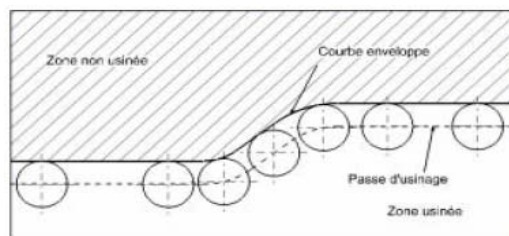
Matière enlevée lors d'une passe d'usinage [7]
